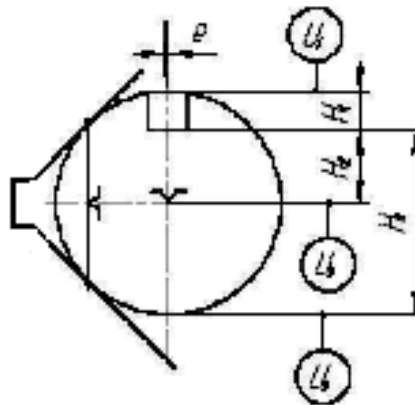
Розташування баз під час встановлення деталі в призму
